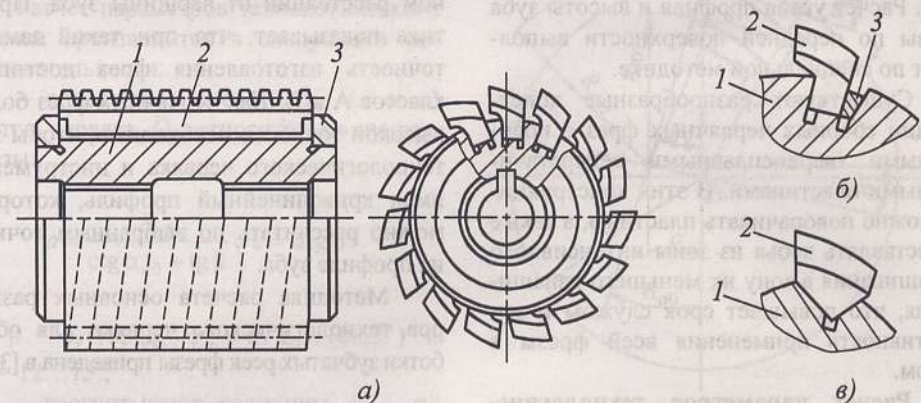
Сборная червячная фреза с поворотными рейками
